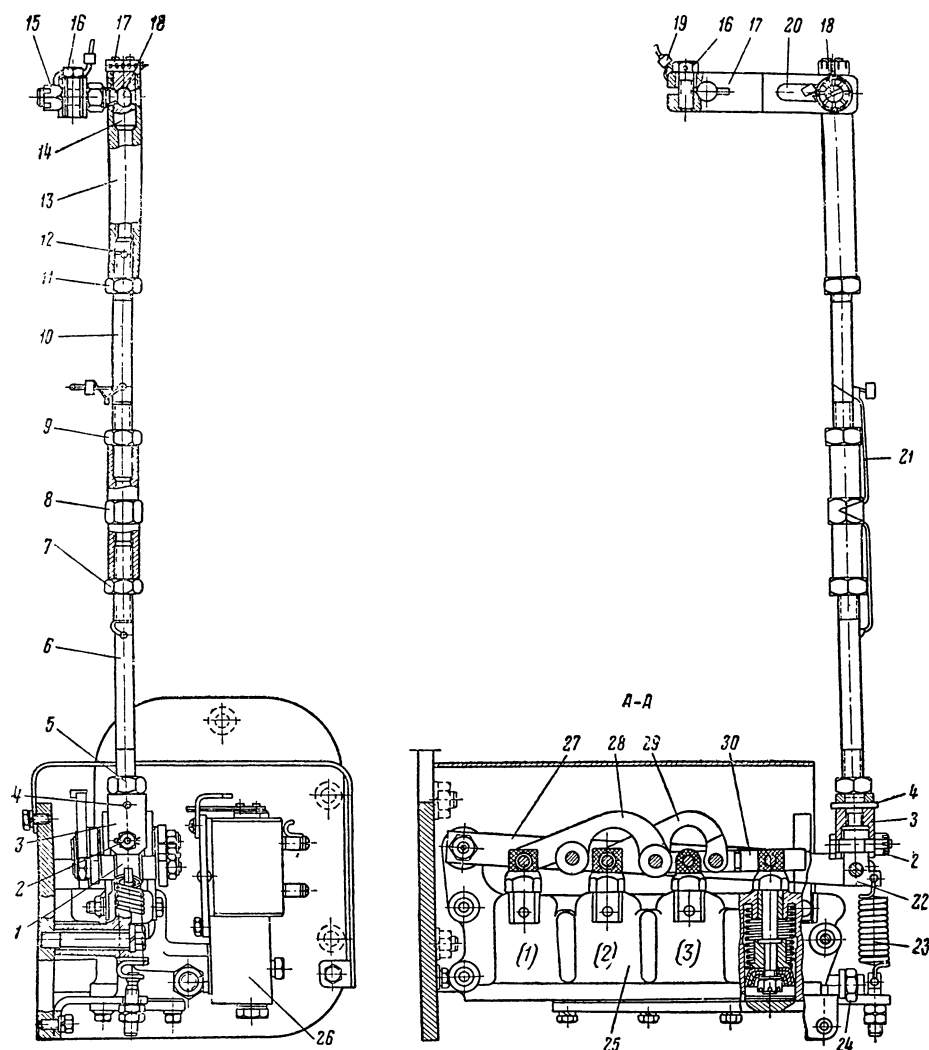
Электропневматический механизм и рычажная передача управления регулятора:
